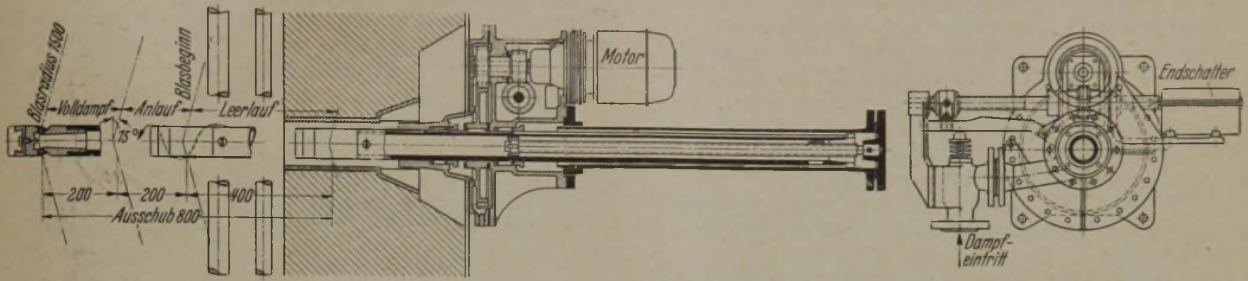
Rückstrahlstoßbläser zur Reinigung der Brennkammer-Kühlflächen. Werkzeugnung Ver. Kesselwerke AG., Düsseldorf.
